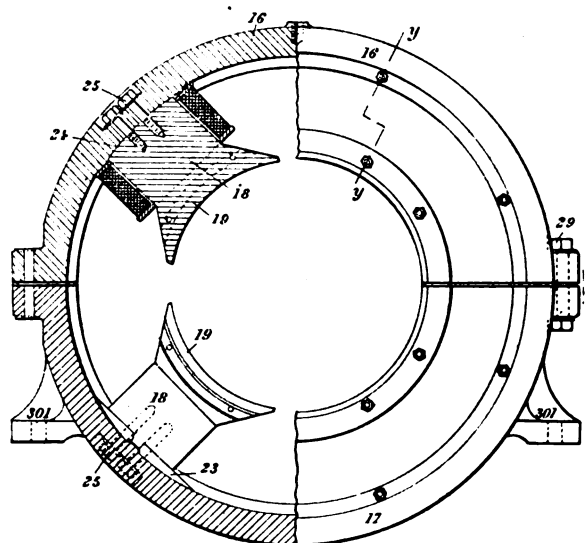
Coupe et vue d'un inducteur de machine à quatre pôles Jackson et Lewis.
